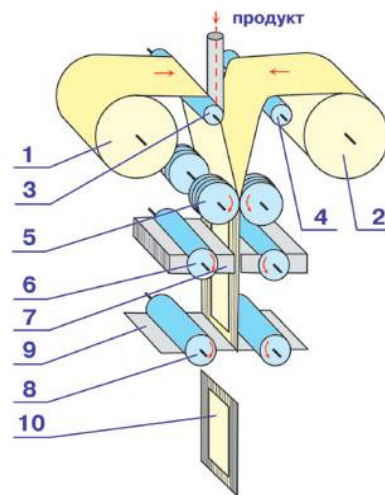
Компонування машини з роторними губками зварювання і механізмами відрізання: 1, 2 – рулони плівки; 3, 4 – направляючі валки; 5 – ролики поздовжнього зварювання; 6, 8 – ротор; 7 – губки поперечного зварювання; 9 – відрізний ніж; 10 – готовий пакет
